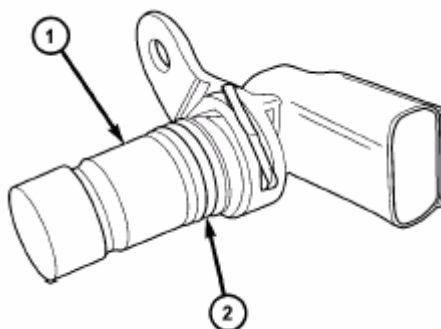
Датчик положения коленчатого вала и уплотнительное кольцо:
